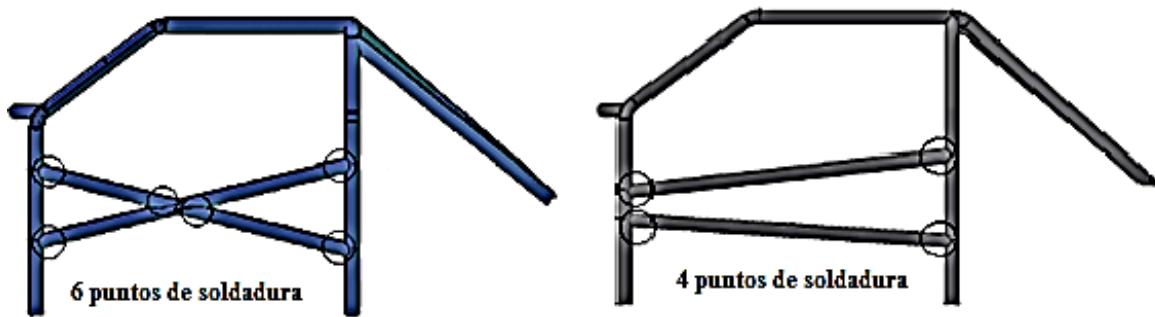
Puntos de soldadura de diseños presentados.
